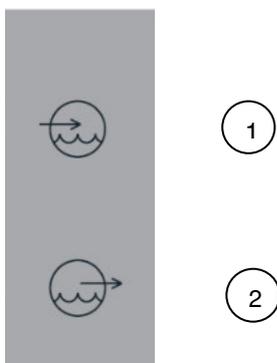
Anschlüsse TIG – COOL CART 1400 / TIG – COOL 1400
